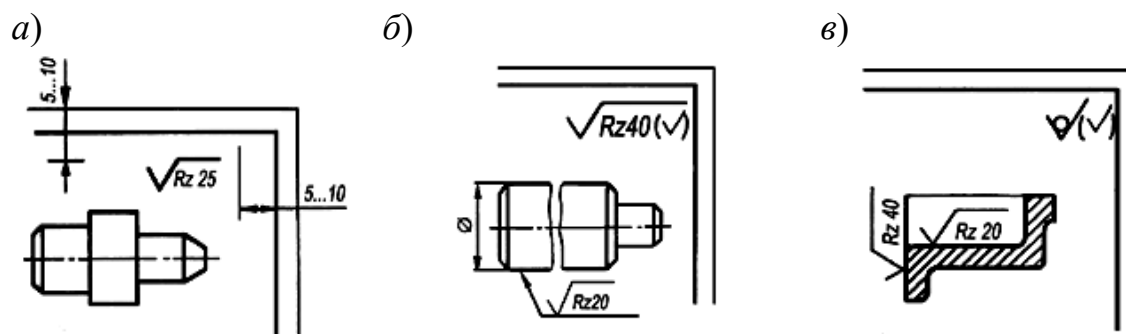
Обозначение одинаковой (а) и преобладающей (б, в) шероховатости
